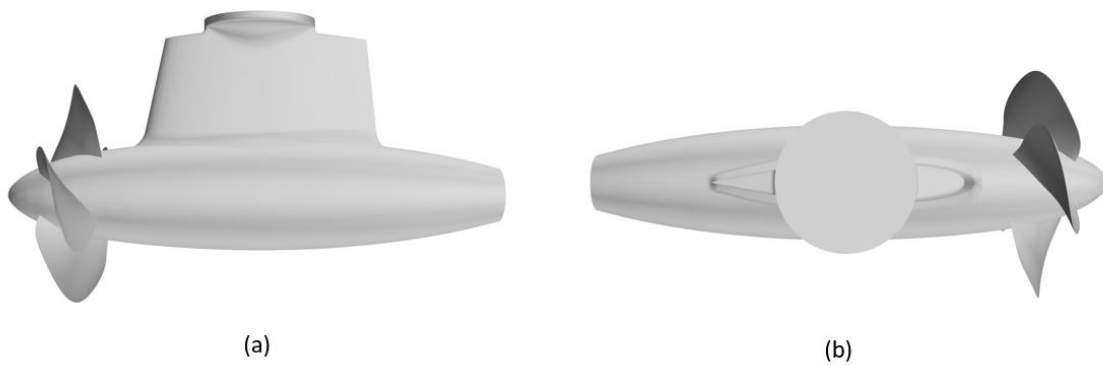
Pod in configurazione *pull*, (a) vista longitudinale, (b) vista in pianta.
